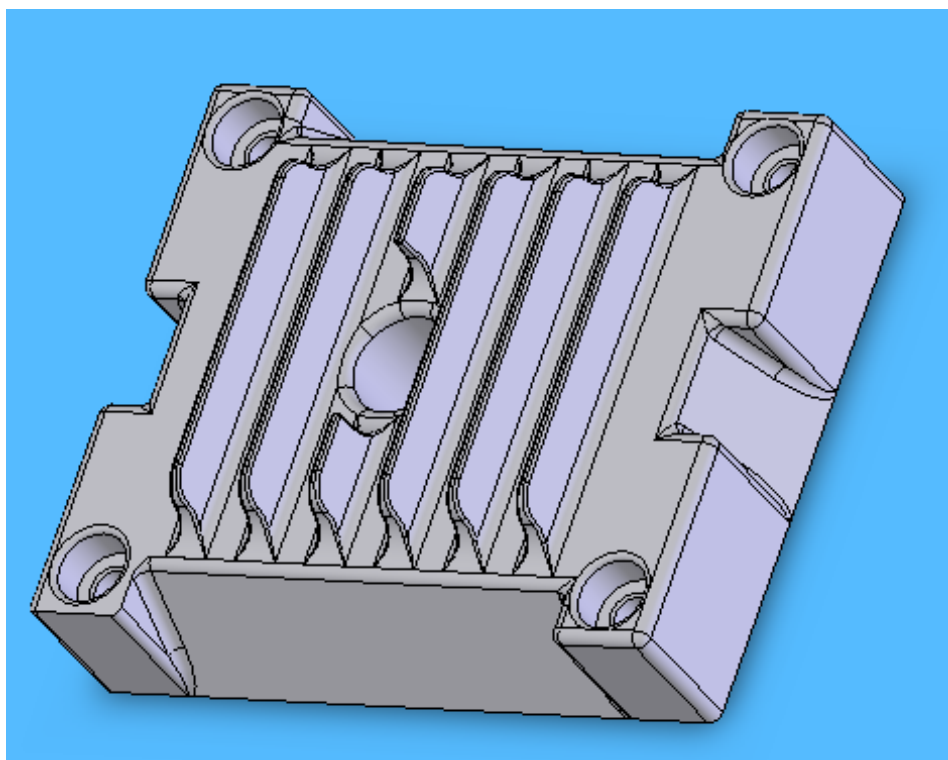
Model hlavy válce motoru – spodní pohled
